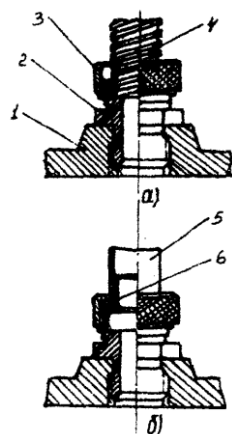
Крепление трубок ПХВ и металлорукавов к корпусу аппарата:
